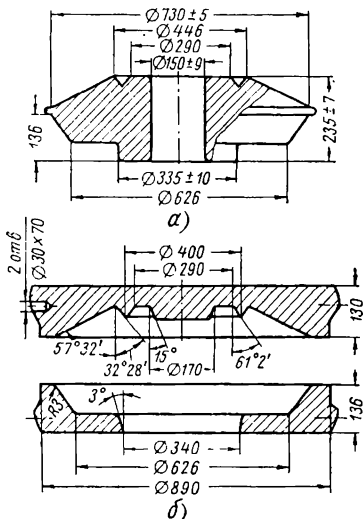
Изготовление поковки конической шестерни: а — поковка; б — подкладной штамп
